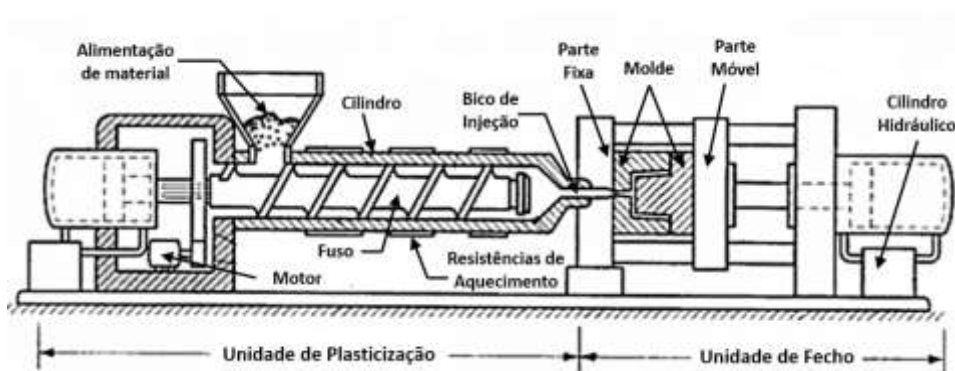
Máquina de moldação por injeção e os seus componentes principais.
